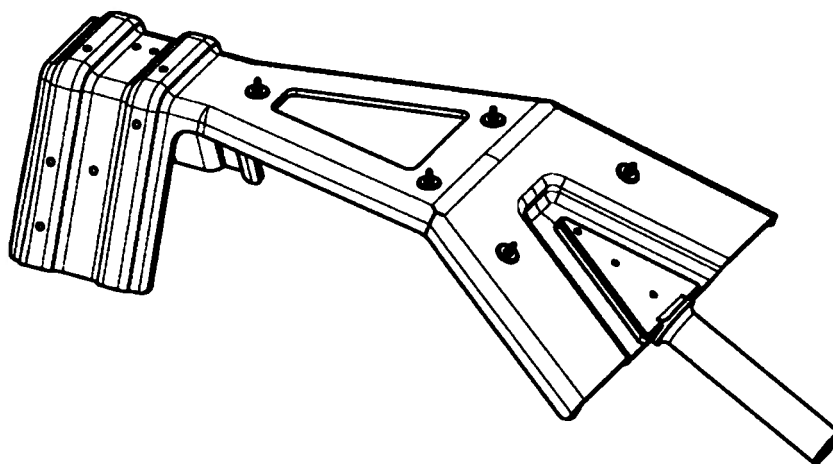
Устройство калибровки АРХМ С-дуга с ППД
